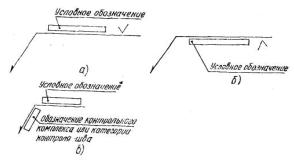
Нанесение обозначения шероховатости механически обработанной поверхности
